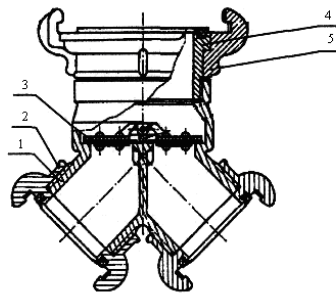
Будова рукавного водозбирача: 1 — корпус вхідного патрубка; 2 — головка з'єднувальна з умовним проходом DN 80; 3 — клапан; 4 — корпус вихідного ніпеля; 5 — з'єднувальна головка з умовним проходом DN 125; 6 — вісь; 7 — кронштейн
